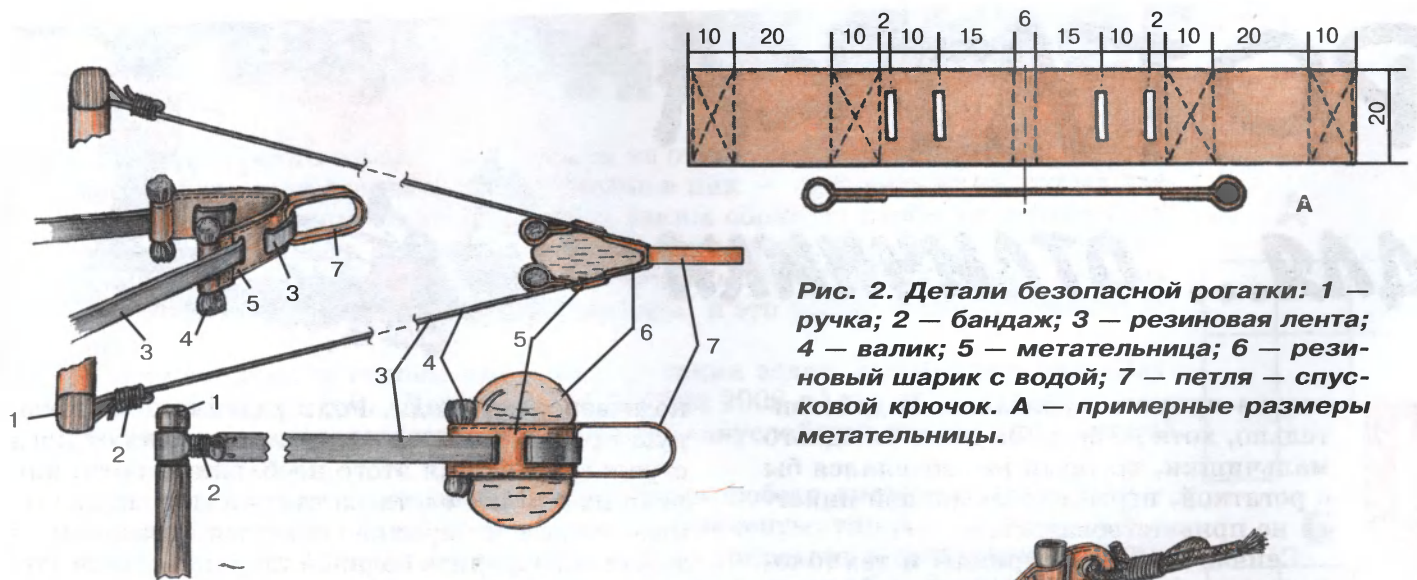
Детали безопасной рогатки: 1 — ручка; 2 — биндаж; 3 — резиновая лента; 4 — валик; 5 — метательница; 6 — резиновый шарик с водой; 7 — петля — спусковой крючок. А — примерные размеры метательницы.
